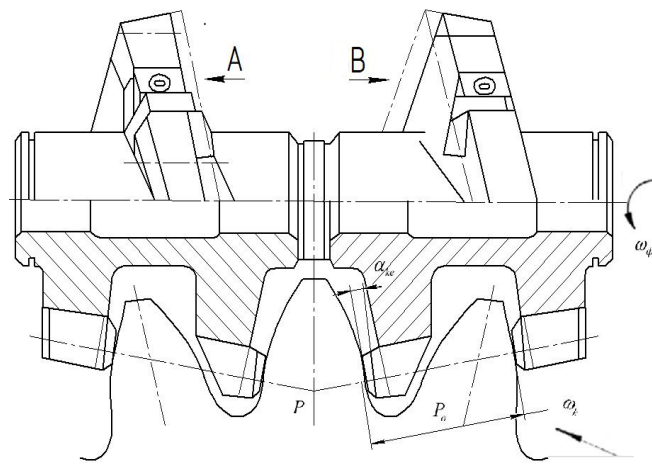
Принципова конструкція фрези з роздільною схемою формоутворення
